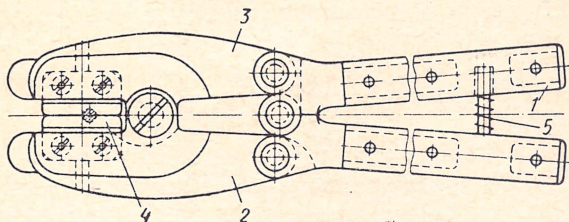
Двухшарнирные ножницы для резки крепежной проволоки
